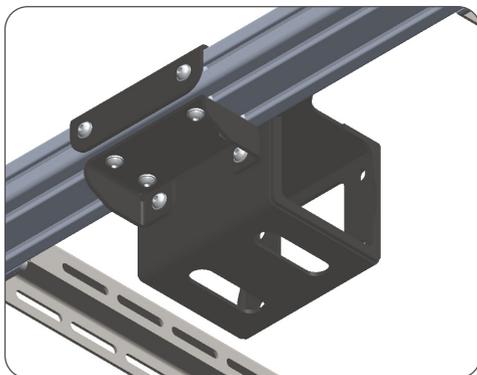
Halter 1.1 von unten/ bracket 1.1 bottom view
